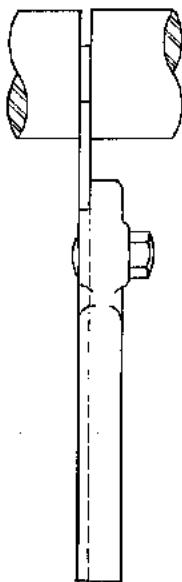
La herramienta de tronzar corta cuando penetra perpendicularmente en la pieza.
